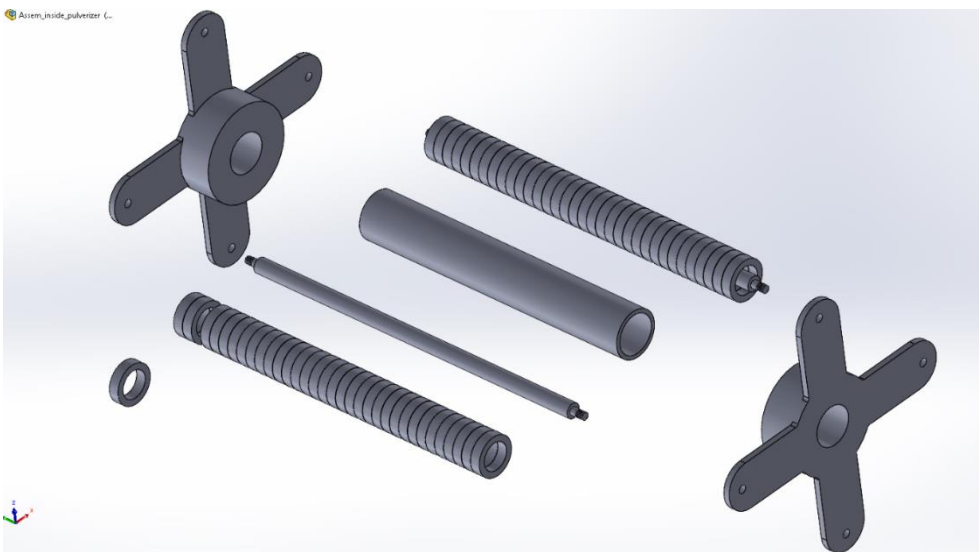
3D-απεικόνιση του Assembly του κόπλερ
